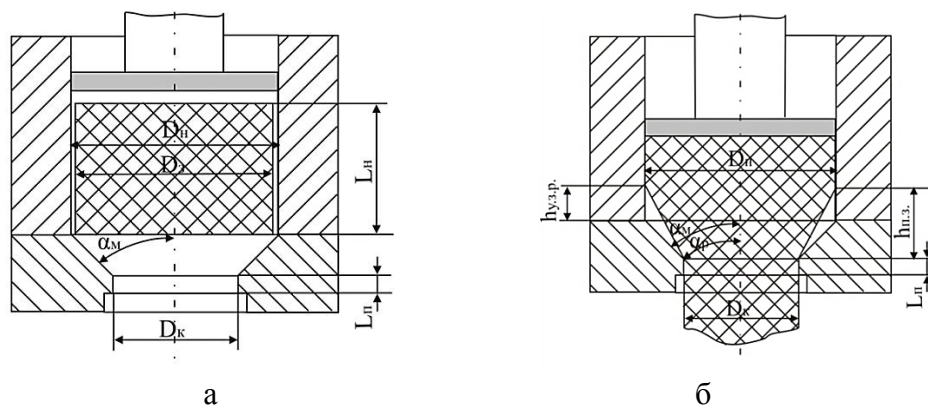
Прессование с прямым истечением сплошного профиля из круглой заготовки через одноканальную матрицу на стадии распрессовки (а) и начала истечения металла (б) [7]
